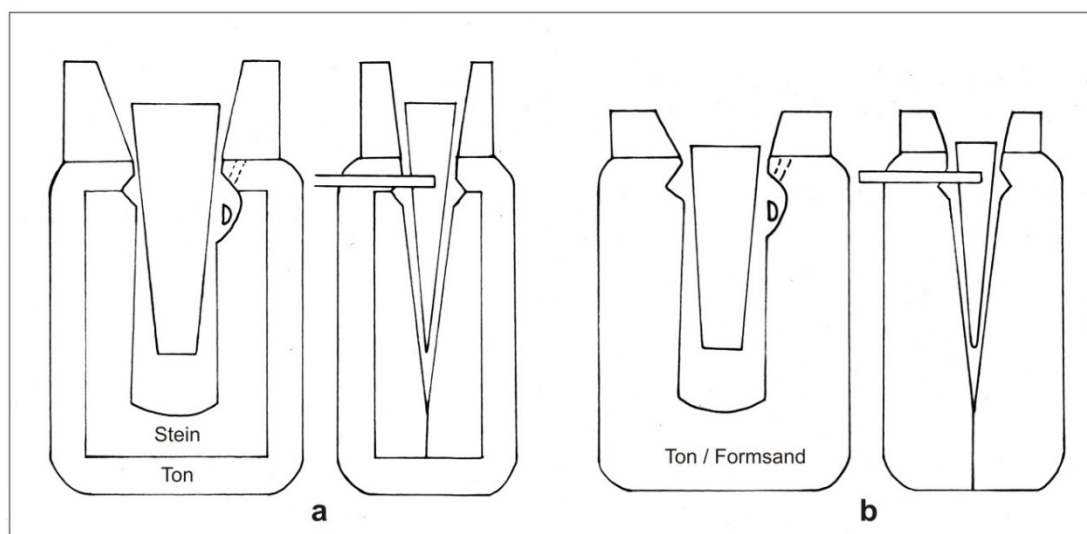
Mögliche Rekonstruktionen der Eingussvariante 7 mit Steinformen (a) und tönernen oder Sandformen (b).
